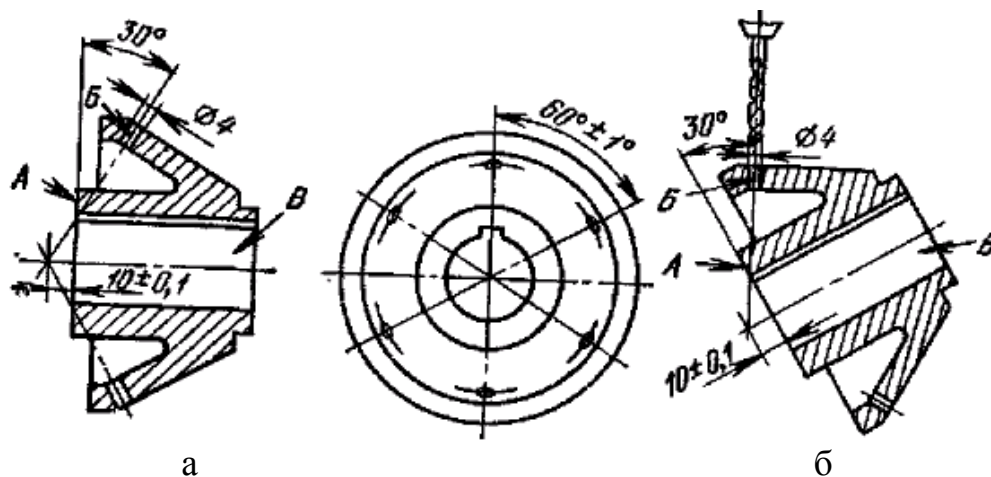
Заготовка для обработки шести отверстий, требующая приспособления.
